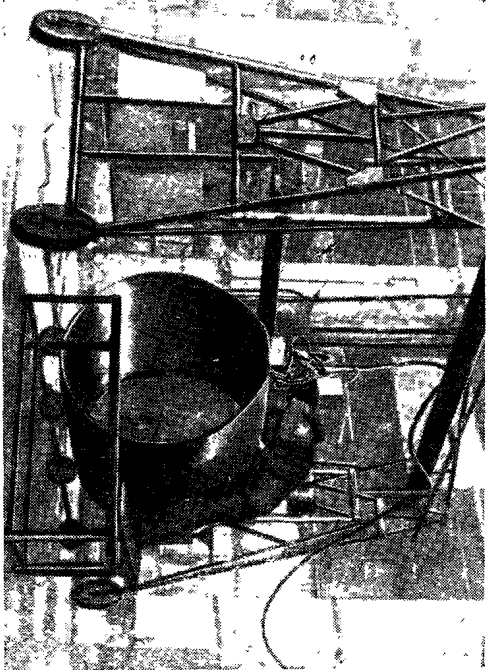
Установка с подъемными путями для сварочного трактора.
